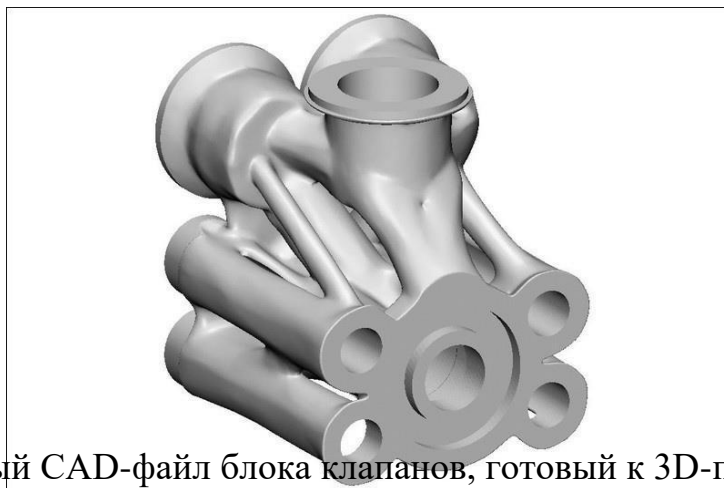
Финальный CAD-файл блока клапанов, готовый к 3D-печати Центр
